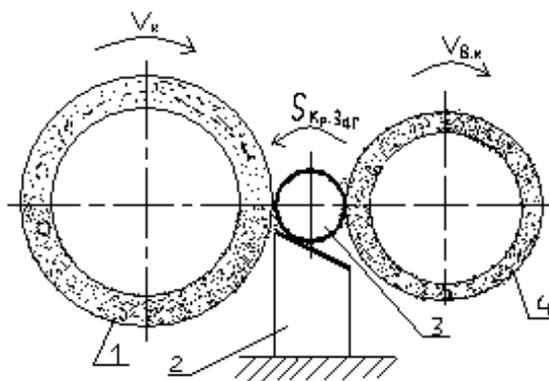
Схема обработки на бесцентрово-шлифовальном станке
